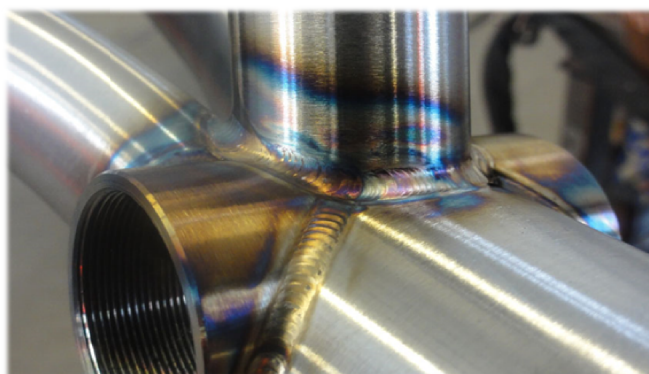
Soldadura TIG en una tubería cruzada
